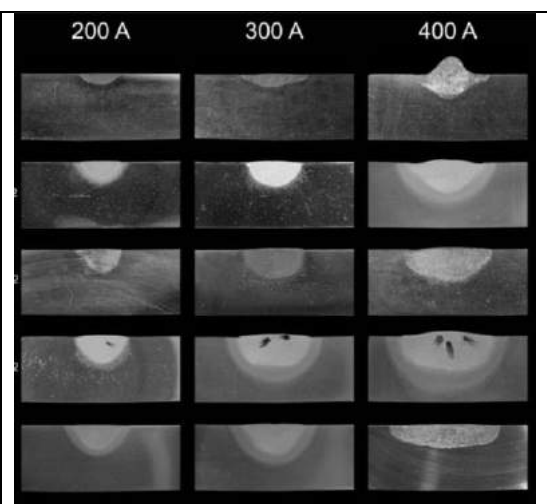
Seções transversais dos cordões cortados a 150 mm do início da soldagem (Schwedersky (1), 2011.)
